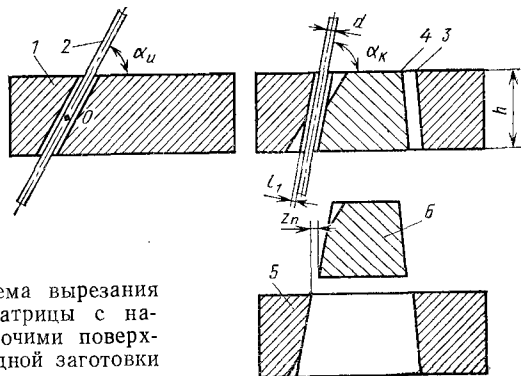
Схема вырезания пуансона и матрицы с наклонными рабочими поверхностями из одной заготовки
